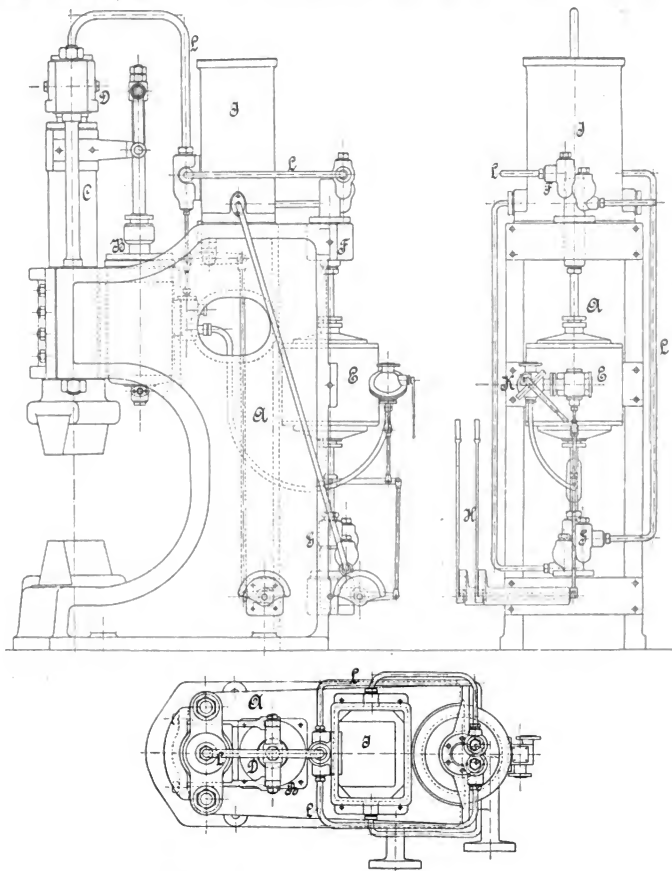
c. Schmiedepresse der Duisburger Maschinenbau-A.-G.
